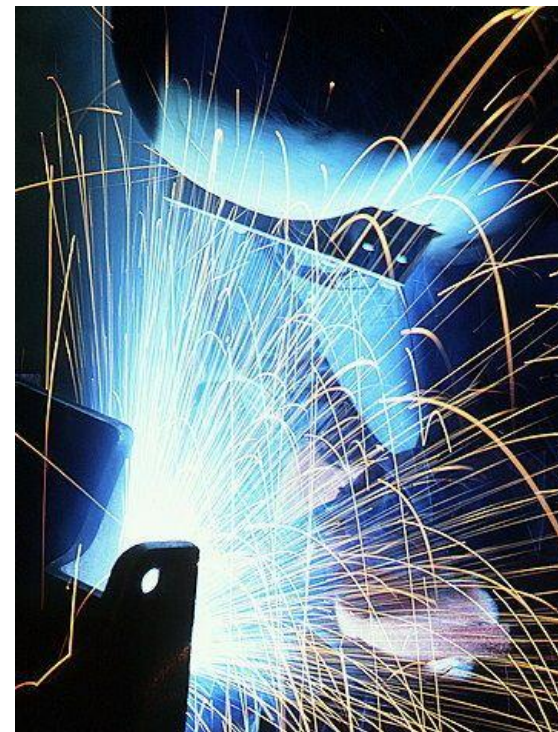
Зона зварювального шва при зварюванні металевими електродами
